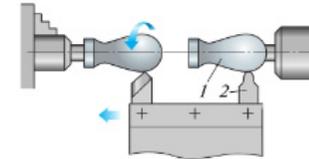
Обработка фасонной поверхности заготовки способом сочетания двух подач с контролем по эталонной детали: 1 — эталонная деталь; 2 — шуп
